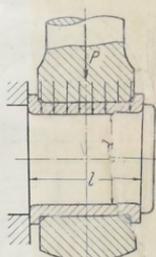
Zur Berechnung eines Stirnzapfens.
